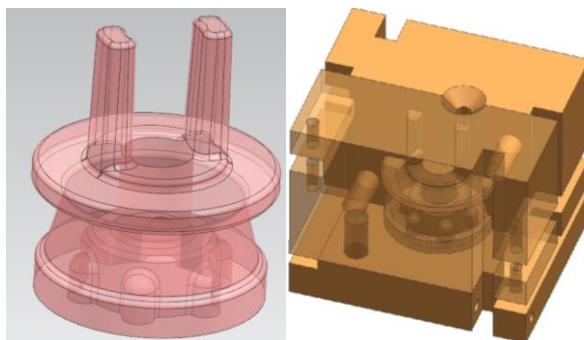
Пресс-форма АО ААК «ПРОГРЕСС» и ЭМ отливки
